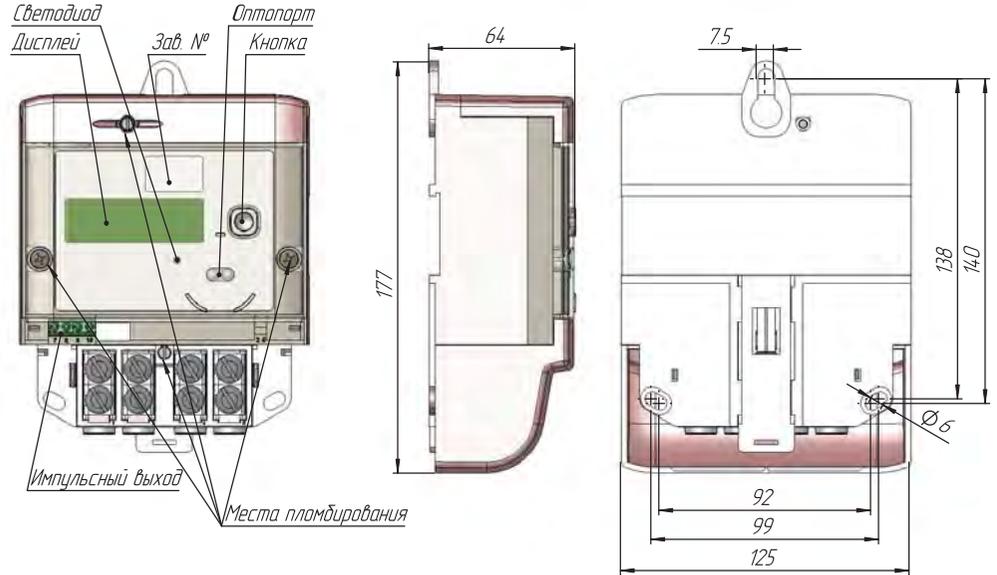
Общий вид, габаритные и установочные размеры, места установки пломб на корпусе однофазного счетчика типа NP-06
